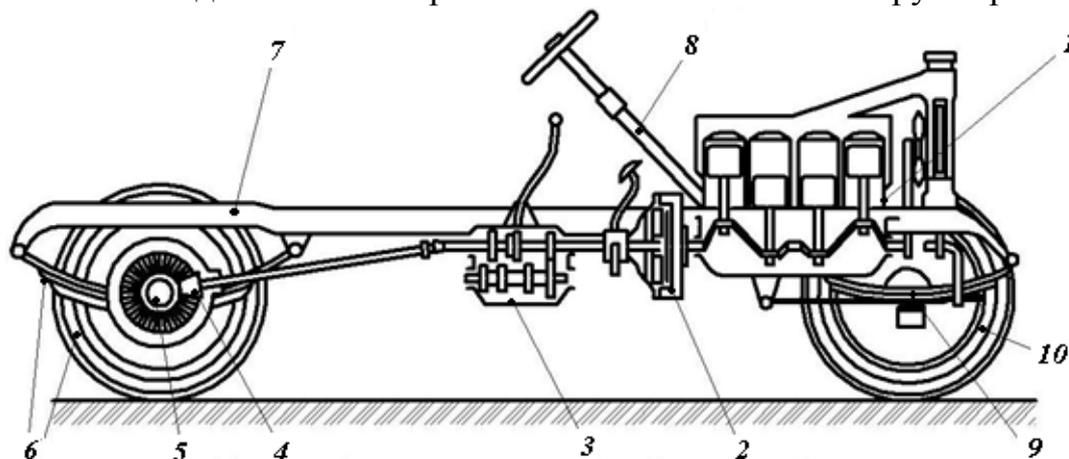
Расположение основных механизмов и сборочных единиц автомобиля:
